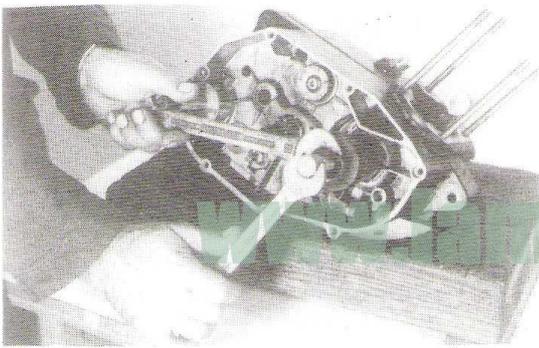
Para desmontar el piñón motor que está fijado al eje cigüeñal, colocar el extractor piñón motor nº 20.53.10.0 de manera que apretando el tornillo del extractor, llegue a dejar suelto el piñón.
